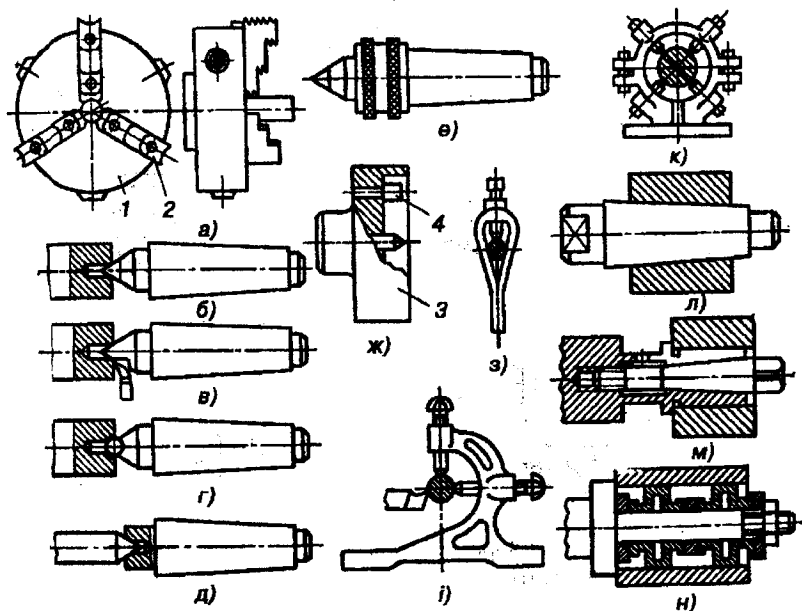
Пристосування для закріплення заготовок на токарних верстатах
